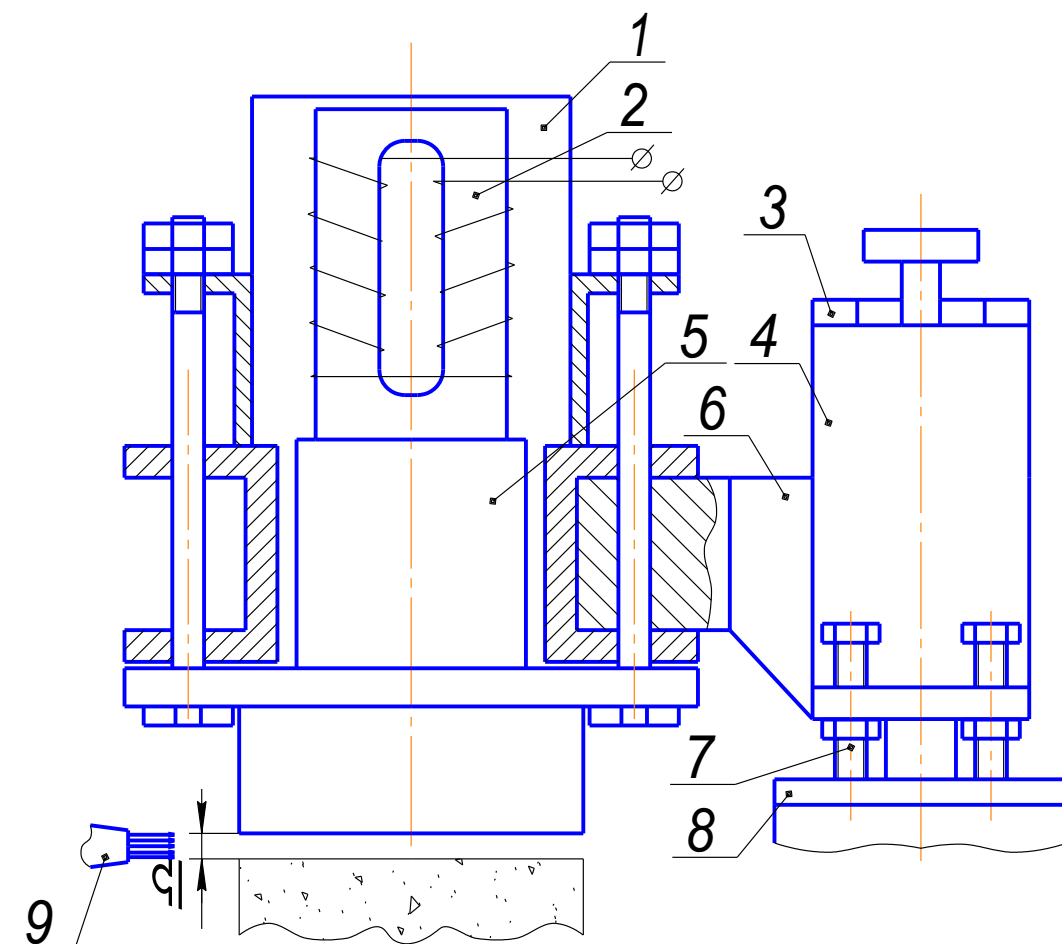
Схема устройства для очистки шлифовального круга
